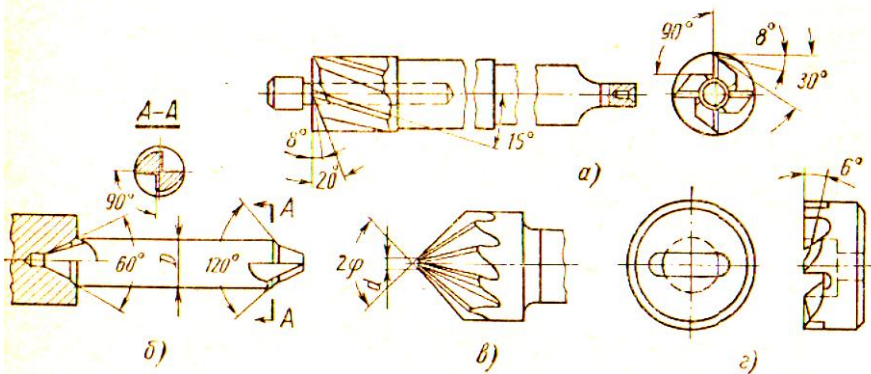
Конструкции зенкеров: а – зенкер для цилиндрических углублений; б – зенковка; в – коническая зенковка; зенкер для зачистки торцовых поверхностей
